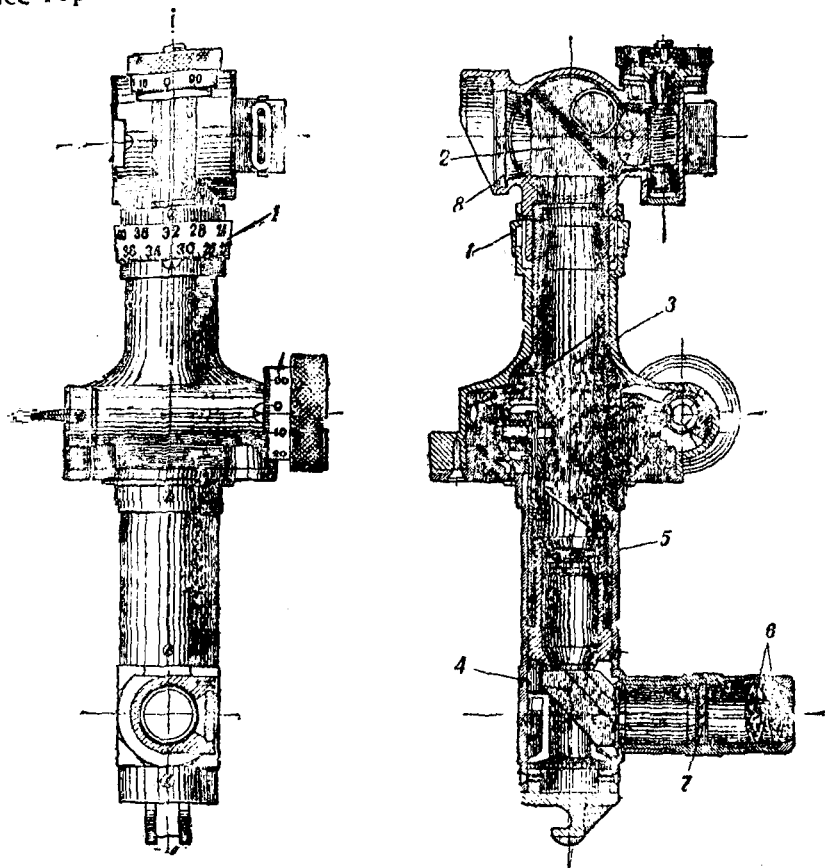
Орудийная панорама. Слева — внешний вид; справа разрез. 1 — угломерное кольцо; 2 — призма-отражатель; 3 — поворачивающая призма; 4 — неподвижная призма; 5 — объектив; 6 — окуляр; 7 — стеклянная пластинка с перекрестием; 8 — защитное стекло.
